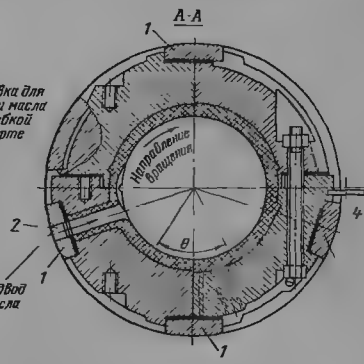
Вкладыш опорного подшипника ЛМЗ.
